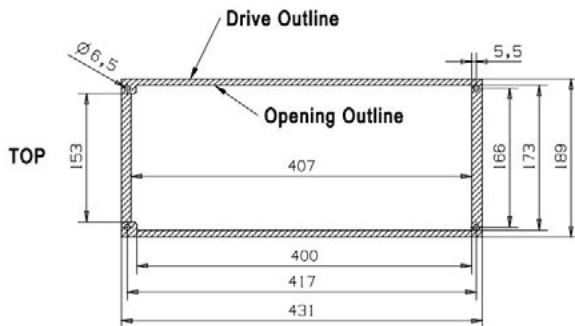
Dimensões do recorte para montagem com flange do MR5 (unidade: mm)
